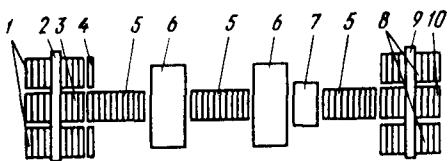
Схема автоматической линии МКШ1 калибровки щитовых заготовок:
